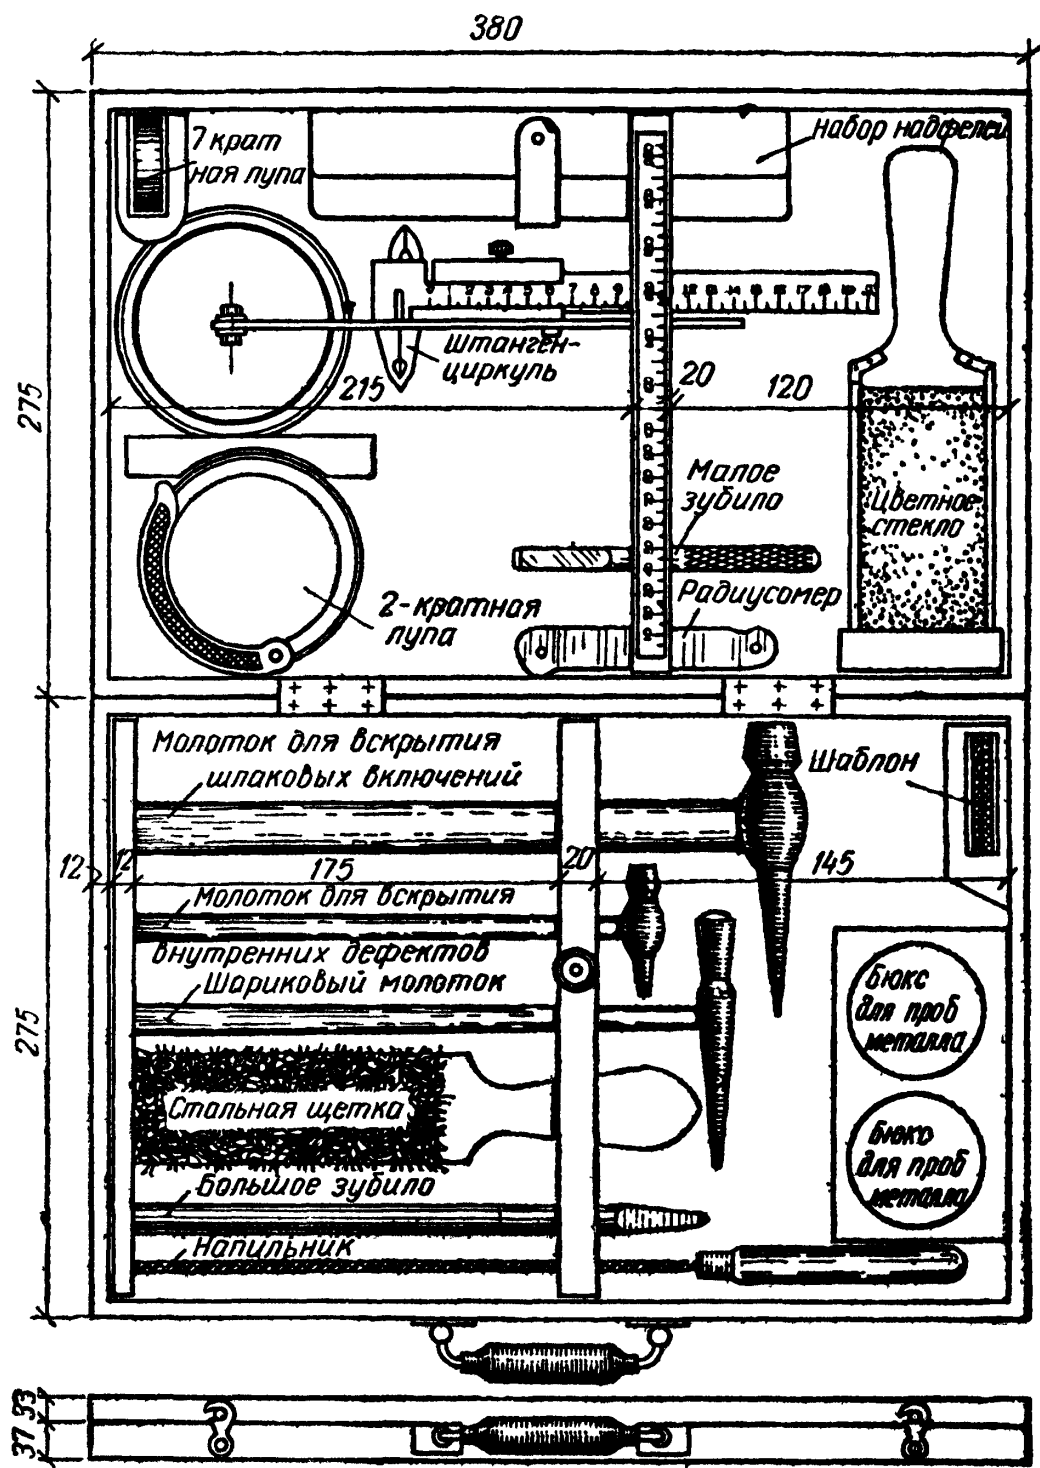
Набор приспособлений и инструмента для полевого контроля качества сварки
